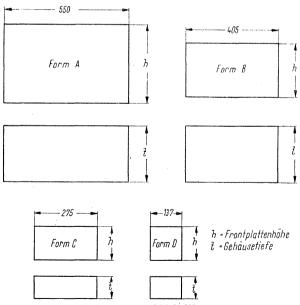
Hauptmaße für Gehäuse nach DIN 41 610
